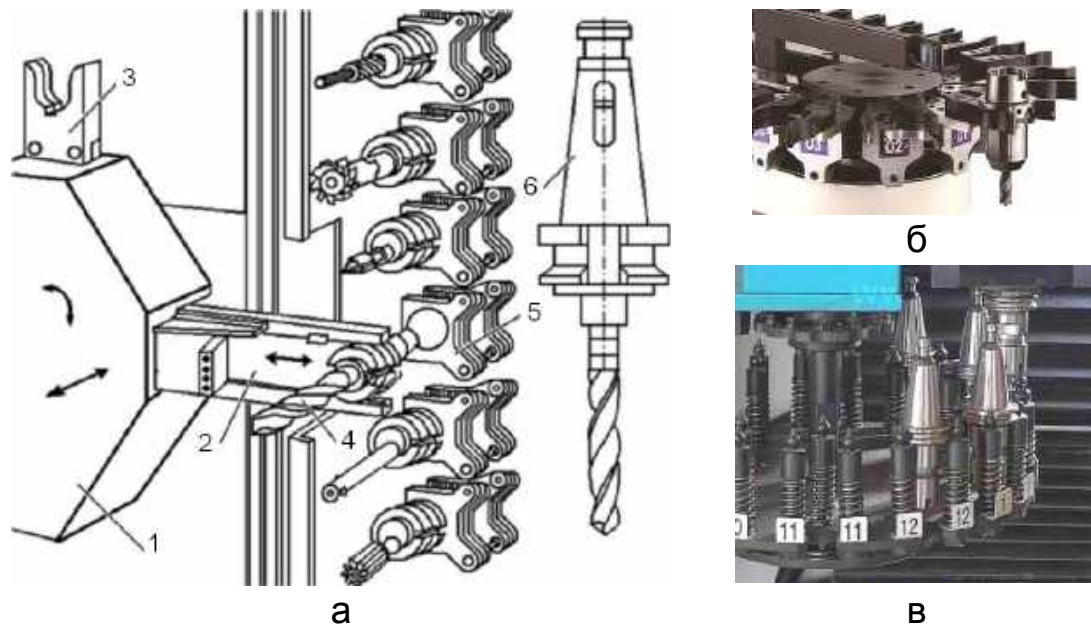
Схема пристрою А3І (а), зовнішній вигляд механізму захоплення (б) та інструментальної обойми (в): 1– корпус захоплювача; 2 – важіль захоплювача; 3 – захоплювач; 4 – інструмент; 5 – гніздо ланцюга інструментальної обойми; 6 – оправка конусна
